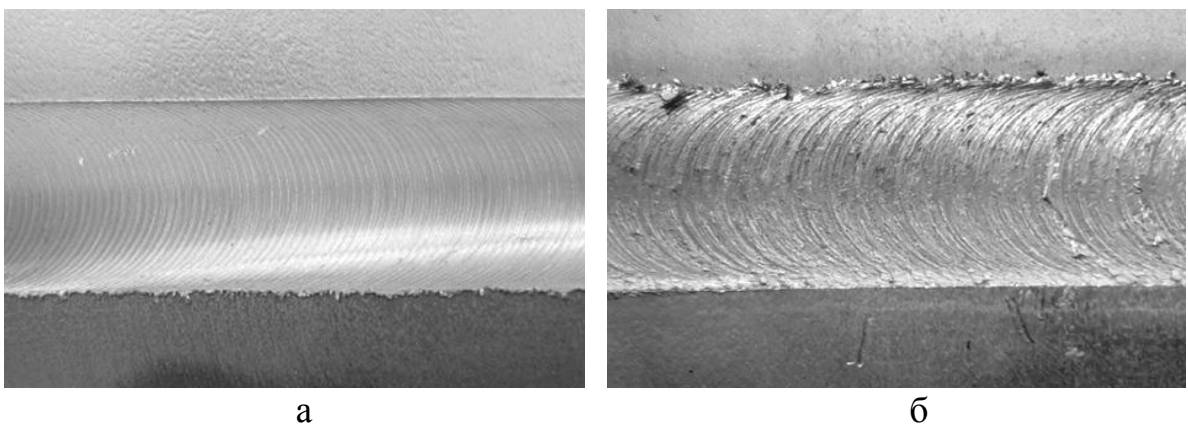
Внешний вид швов сплава 1565чН116 при сварке на воздухе (а) и в ванне с проточной водой (б) [153]
